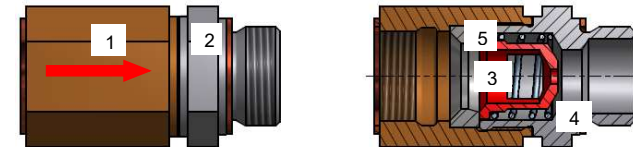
→ PDV (Eintrittseite Innengewinde, Austrittseite Außengewinde)
